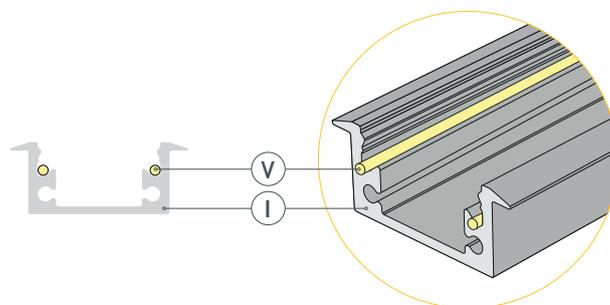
Установка уплотнительной резинки (V) в пазы профиля (I)
